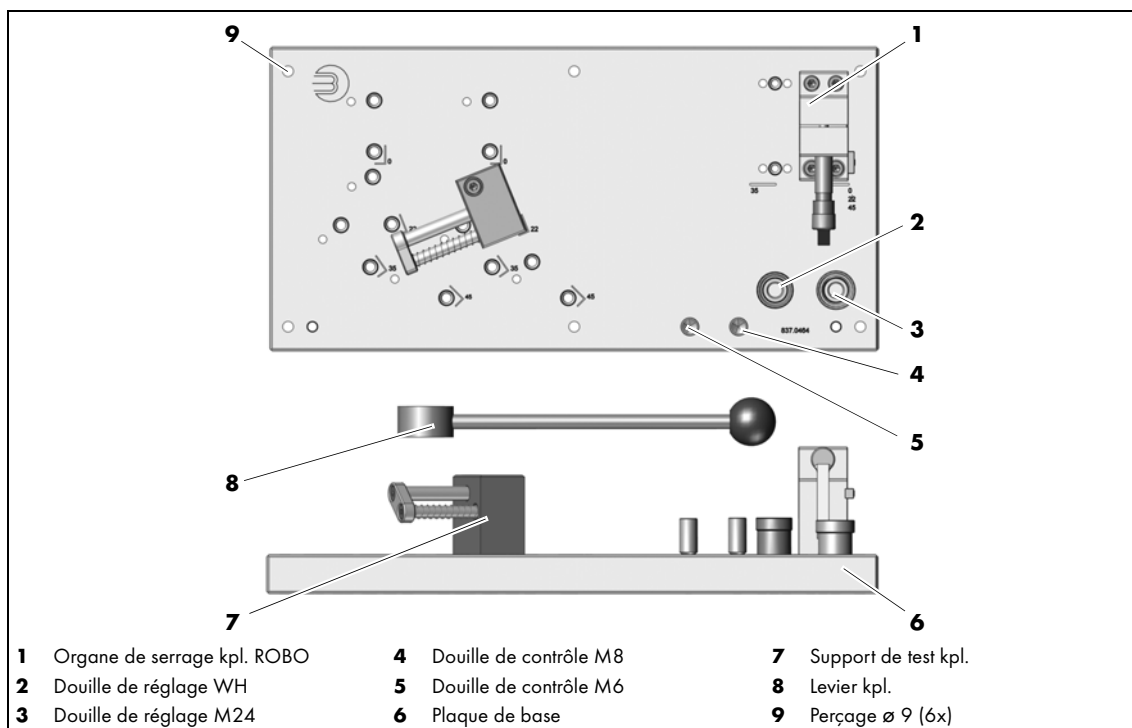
Installer le marbre de contrôle et de rectification VTS-Interlock
